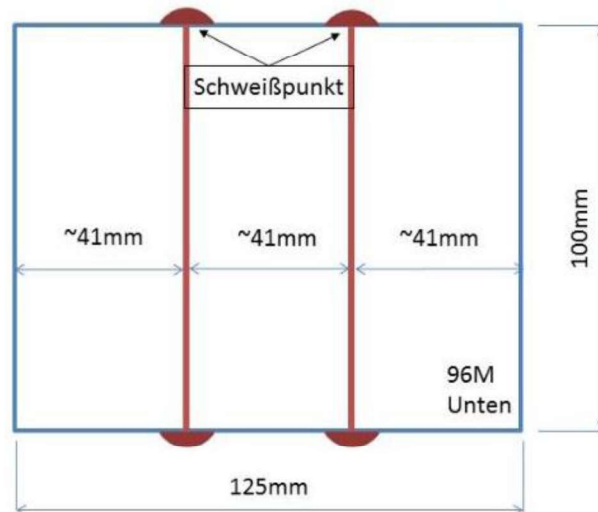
Prinzipskizze Probe mit Schweißpunkt
